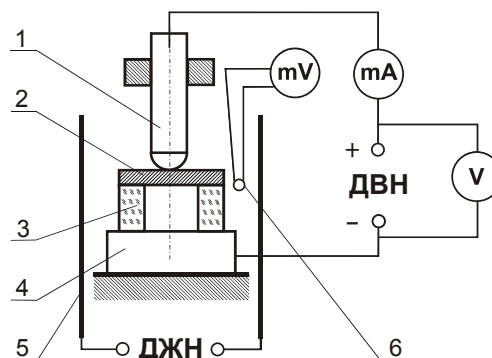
Схема зварювання в твердій фазі в електростатичному полі:
